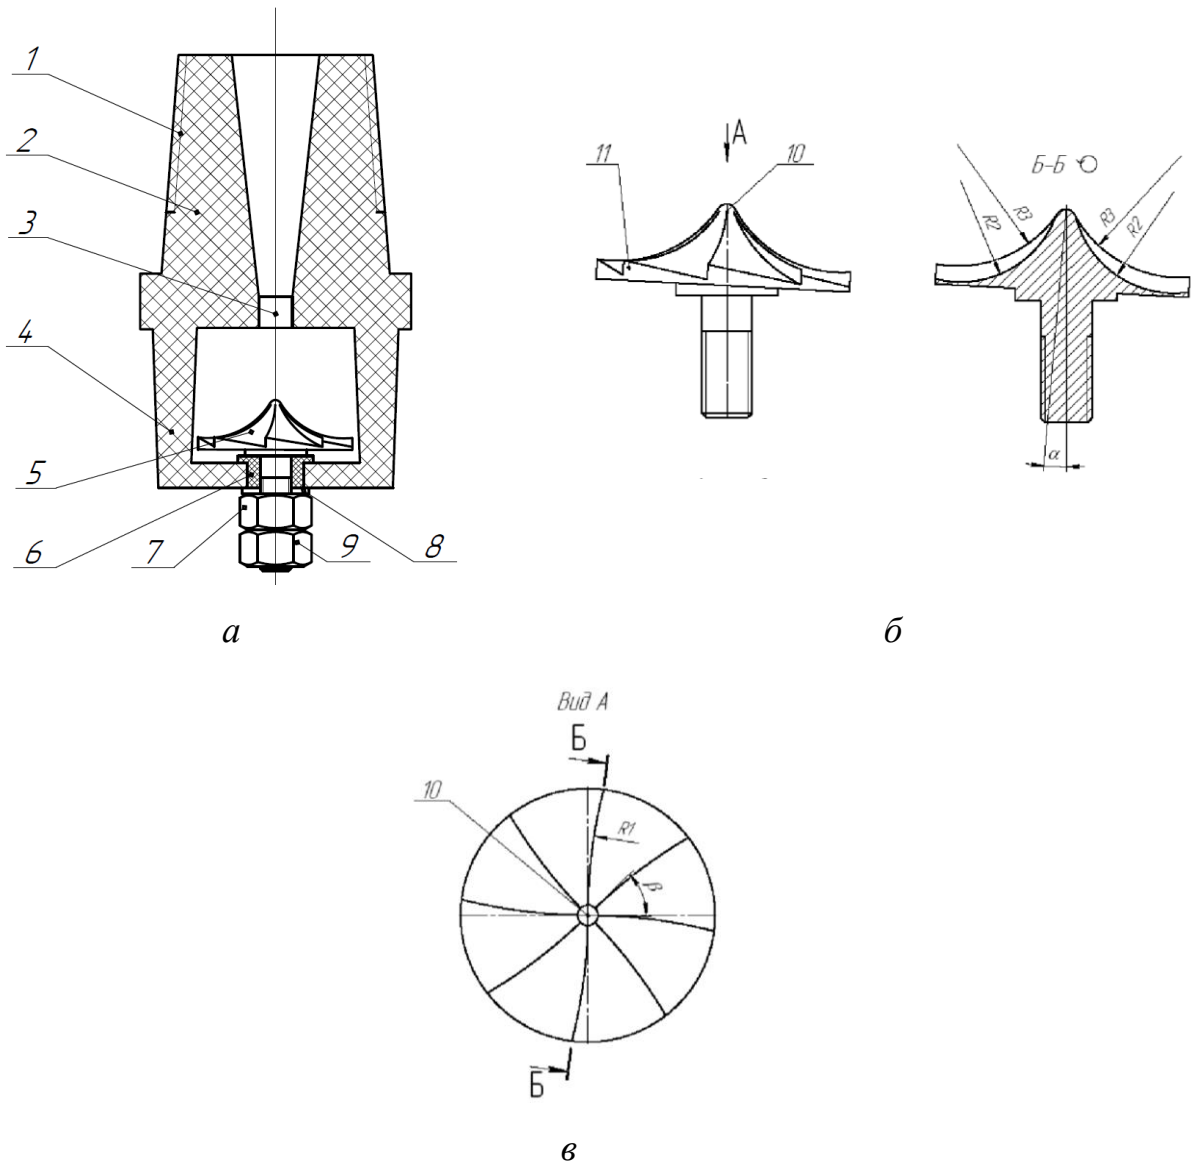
Предлагаемая дождевальная насадка с вращающимся дефлектором конусообразной формы с рифленой поверхностью: *а* – общий вид; *б, в* – вращающийся дефлектор (соответственно вид сбоку и сверху): 1 – резьба; 2 – корпус; 3 – сопло; 4 – ножки; 5 – дефлектор; 6 – втулка; 7 – гайка; 8 – шайба; 9 – контргайка; 10 – бульб; 11 – уступ
